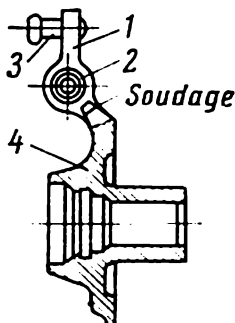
Ensemble soudé d'une voiture automobile
